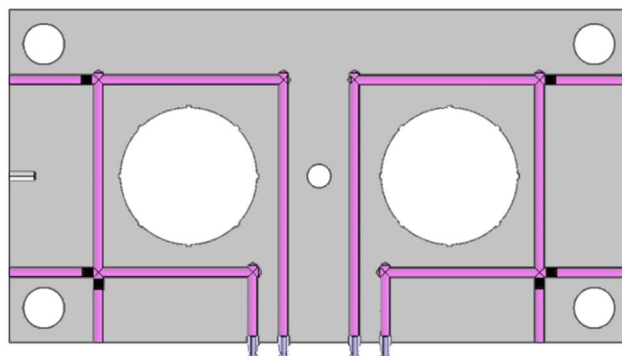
Proudění chladicího média spodním a horním okruhem.
